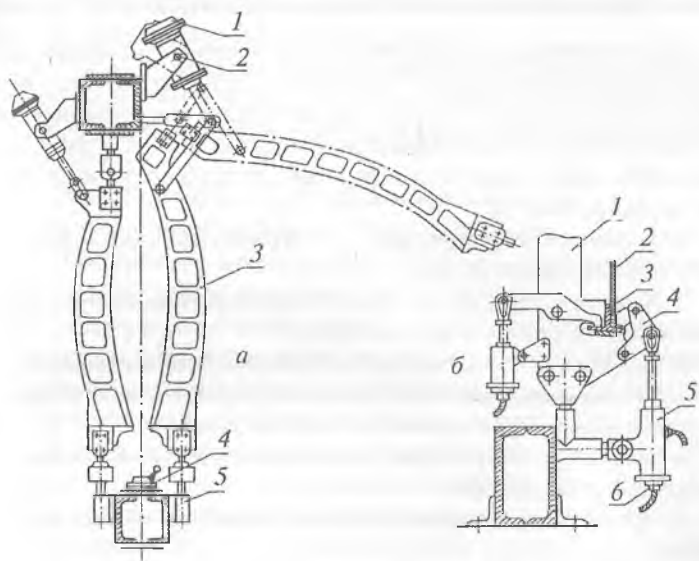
Примеры оснащения сборочных приспособлений средствами механизации: а — гидроподъемники для подъема рубильников: 1 — гидроподъемник; 2 — кронштейн; 3 — рубильник; 4 — фиксатор; 5 — стакан; б — гидравлический зажим: 1 — ложемент; 2 — стенка лонжерона; 3 — пояс лонжерона; 4 — прижим; 5 — гидроцилиндр; 6 — штуцер
